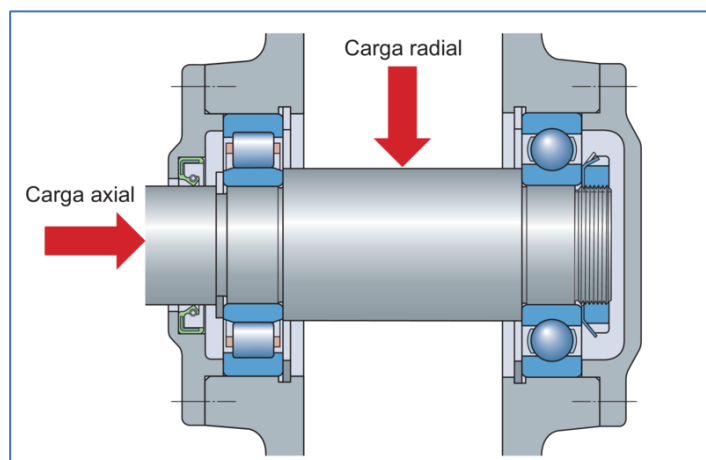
Cargas, fuente SKF. (2015) Cargas axiales y radiales. [imagen] Rodamientos SKF. <https://www.skf.com/es/products/rolling-bearings>
